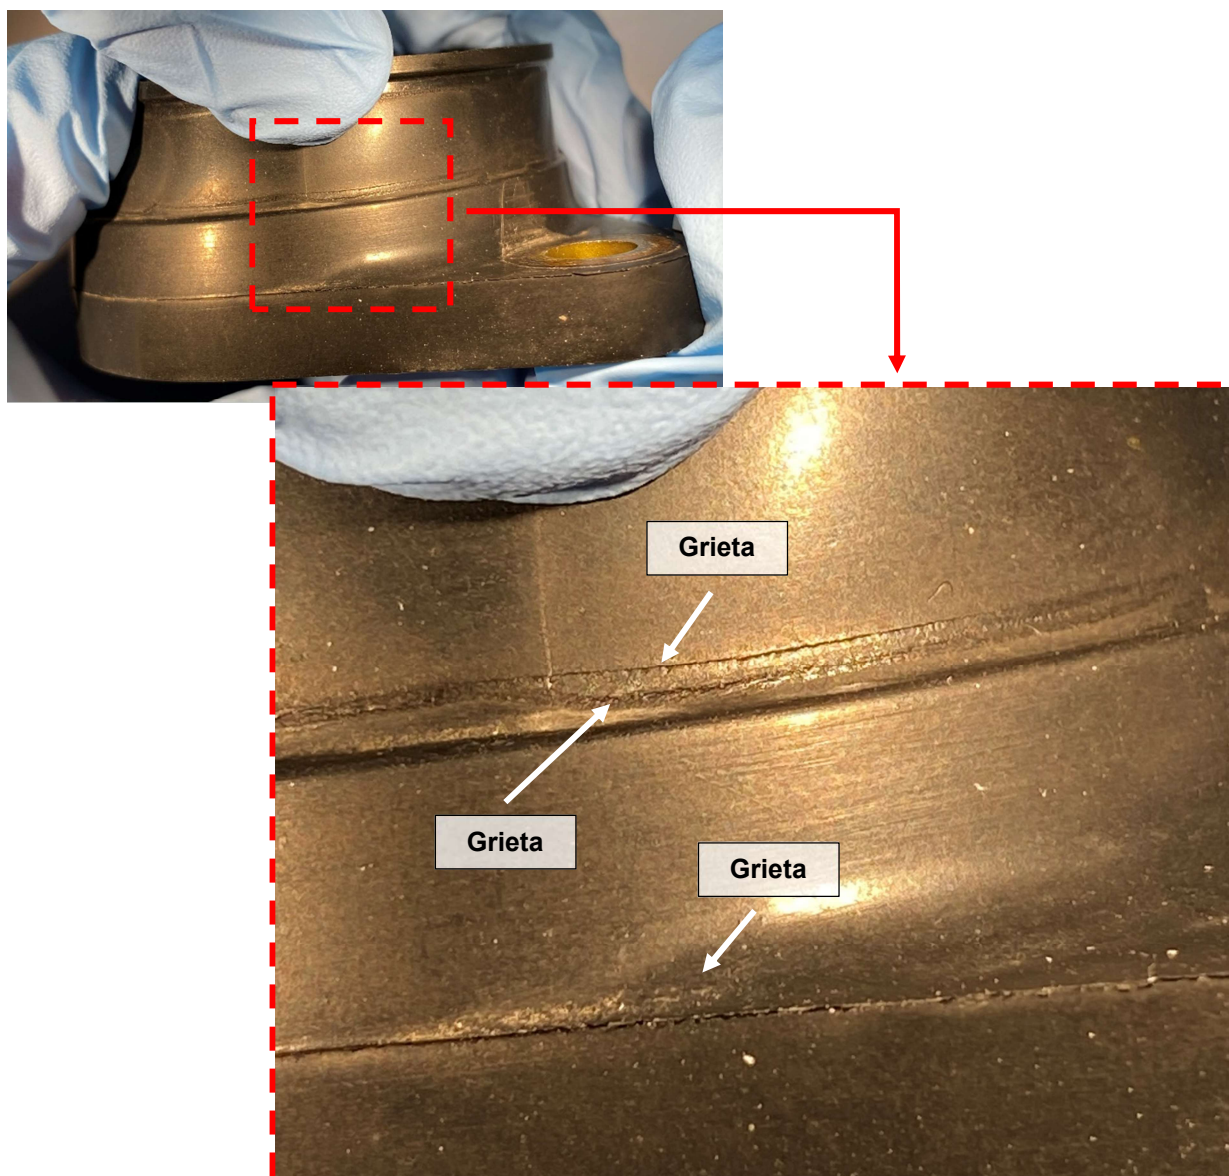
Grietas en la cara exterior del manguito del carburador izquierdo.
